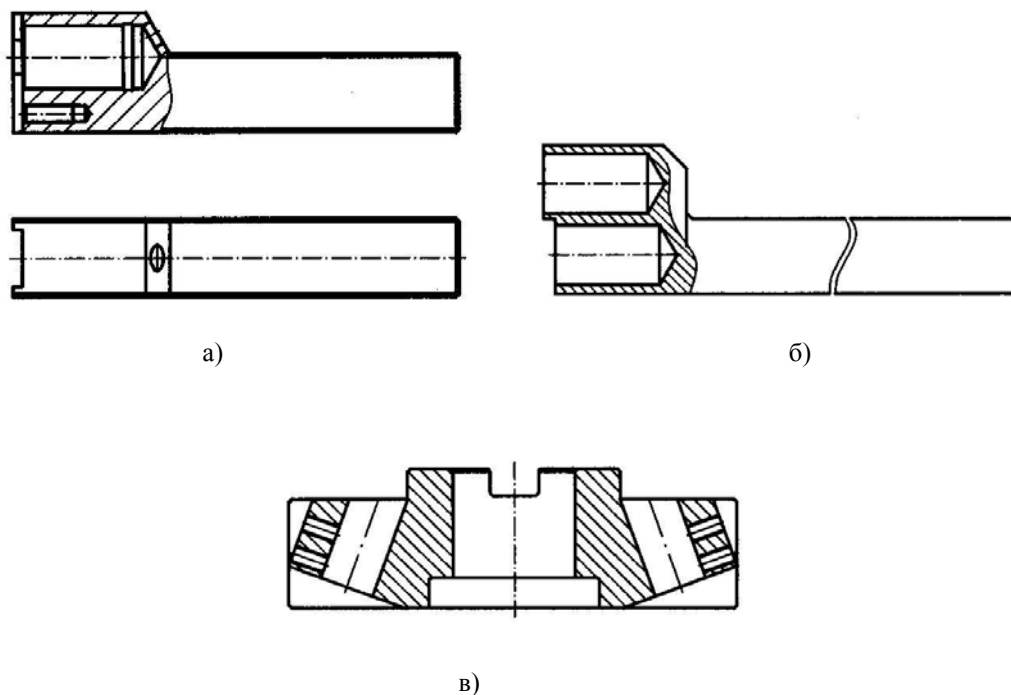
Варианты корпусов блочно-модульных режущих инструментов для: а – токарного резца; б – резца специального с дополнительным лезвием; в – зенкера
